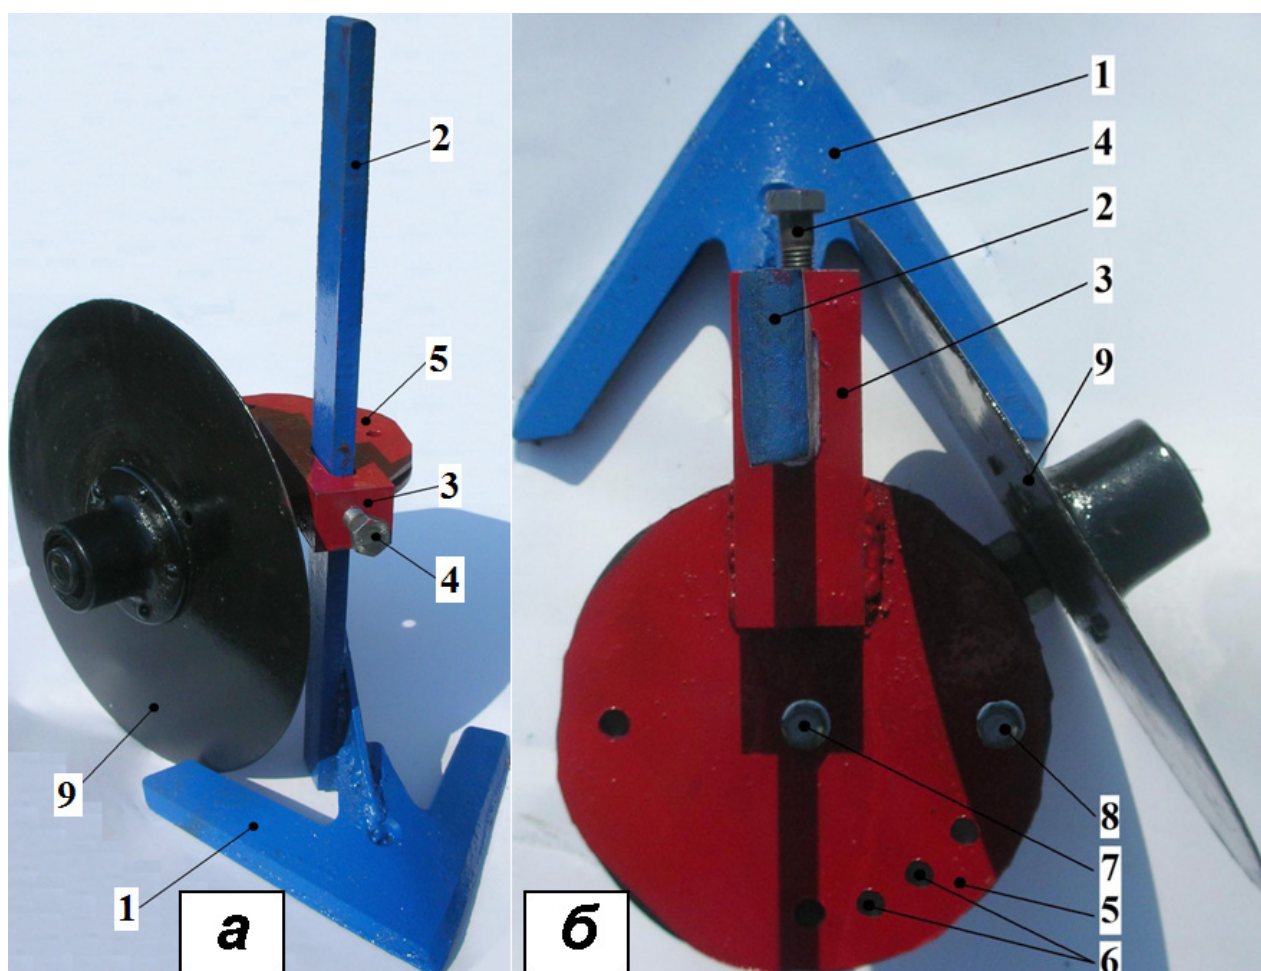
Рабочий орган пропашного культиватора: а – общий вид; б – вид сверху; 1 – стрелчатая лапа; 2 – стойка; 3 – кронштейн; 4 – фиксатор; 5 – регулировочный диск; 6 – отверстия; 7, 8 – болты; 9 – плоский диск
